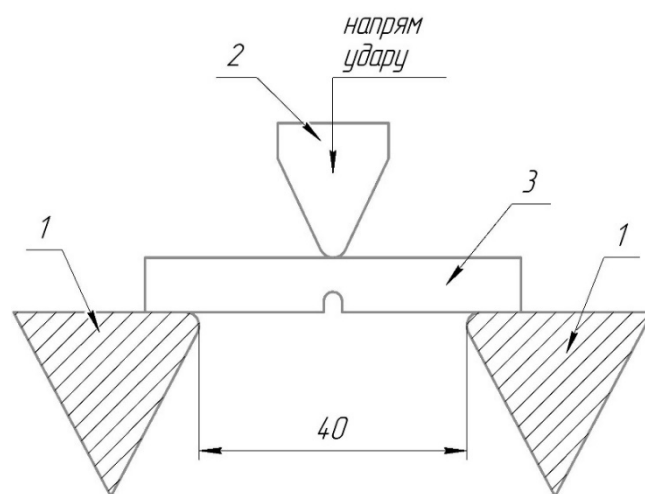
Схема розміщення зразка типу U для випробовування на ударний вигин за Шарпі: 1 – опора копра; 2 – ударник копра; 3 – зразок сталі
